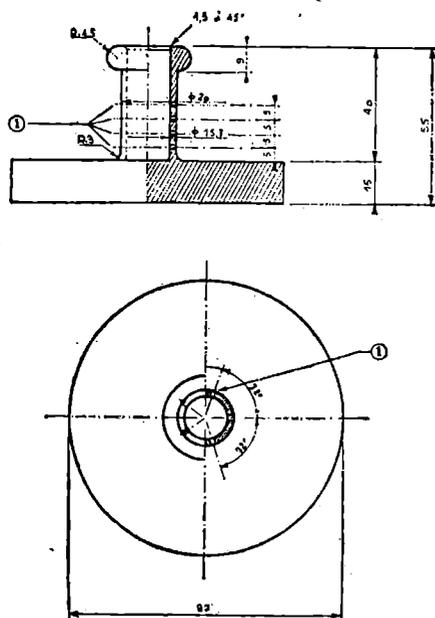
Cilindro hueco de bronce cerrado por un lado: planta y sección vertical (Dimensiones en mm.)
